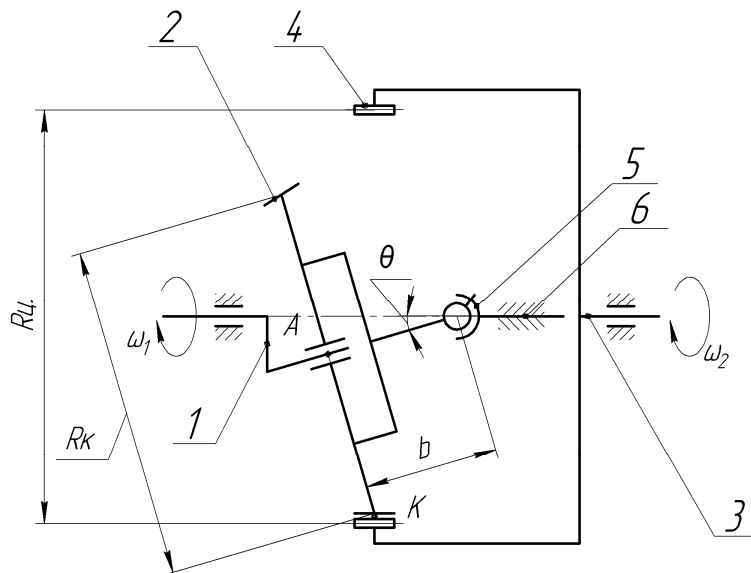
Структурная схема прецессионной роликовой передачи с наружным зубчатым венцом сателлита, связанного с корпусом передачи с помощью угловой муфты
